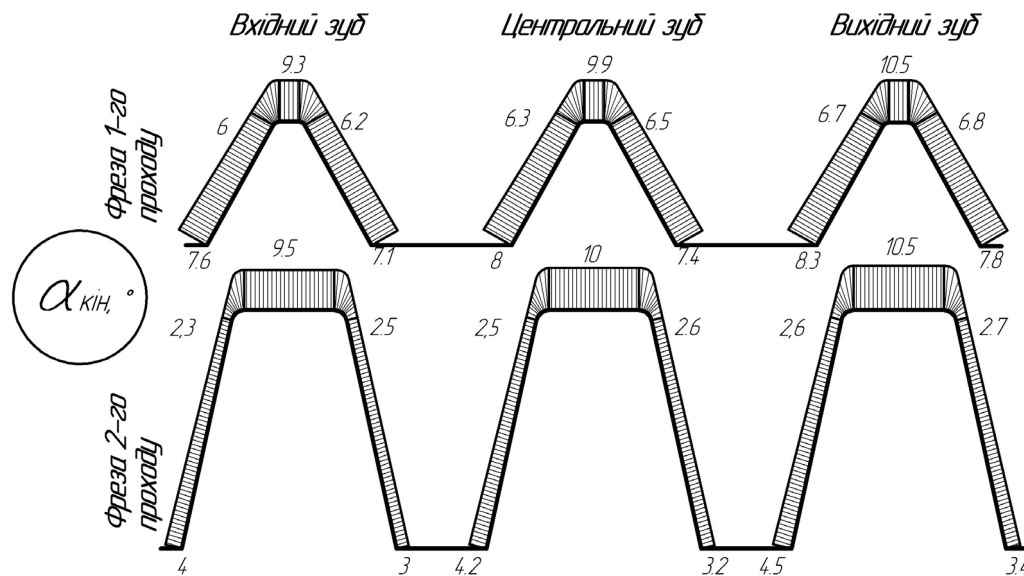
Епюра розподілу задніх кінематичних кутів по профілю зуба фрези для фрез першого проходу та другого проходу за третім способом двох прохідного зубофрезерування табл. 1, кут вихідної інструментальної рейки – фрези першого проходу – 40° , фрези другого проходу – $14,5^\circ$
